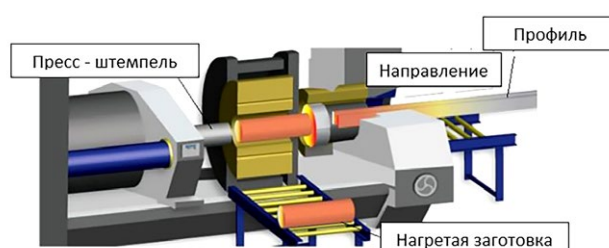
Установка заготовки в контейнер и прессование (экструзия) профиля.
